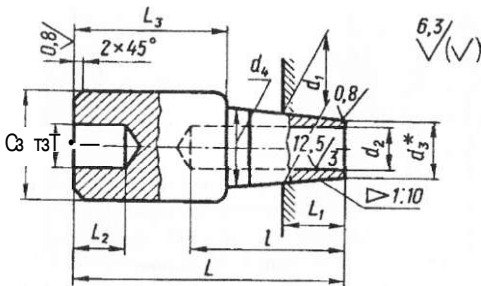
Форма электродів із плоскою робочою поверхнею для рельєфного зварювання (розроблені Запорізьким ПКТІ Автопромзварювання. Галузева нормаль ОН 37.772-70)
